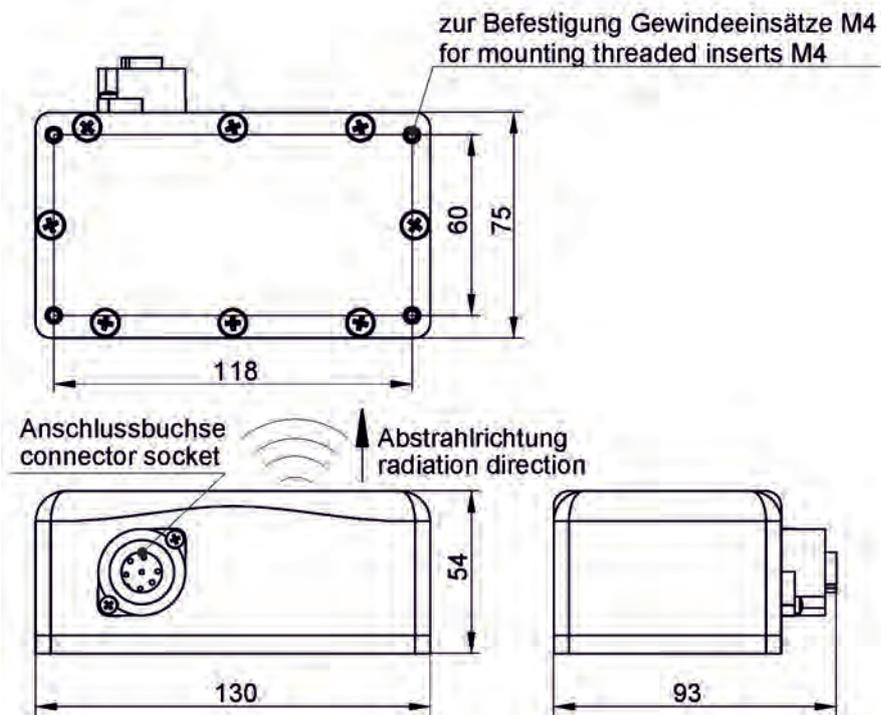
Abmessungen OFR-Radarsensor Typen G00/EV0 im Sensorgehäuse
